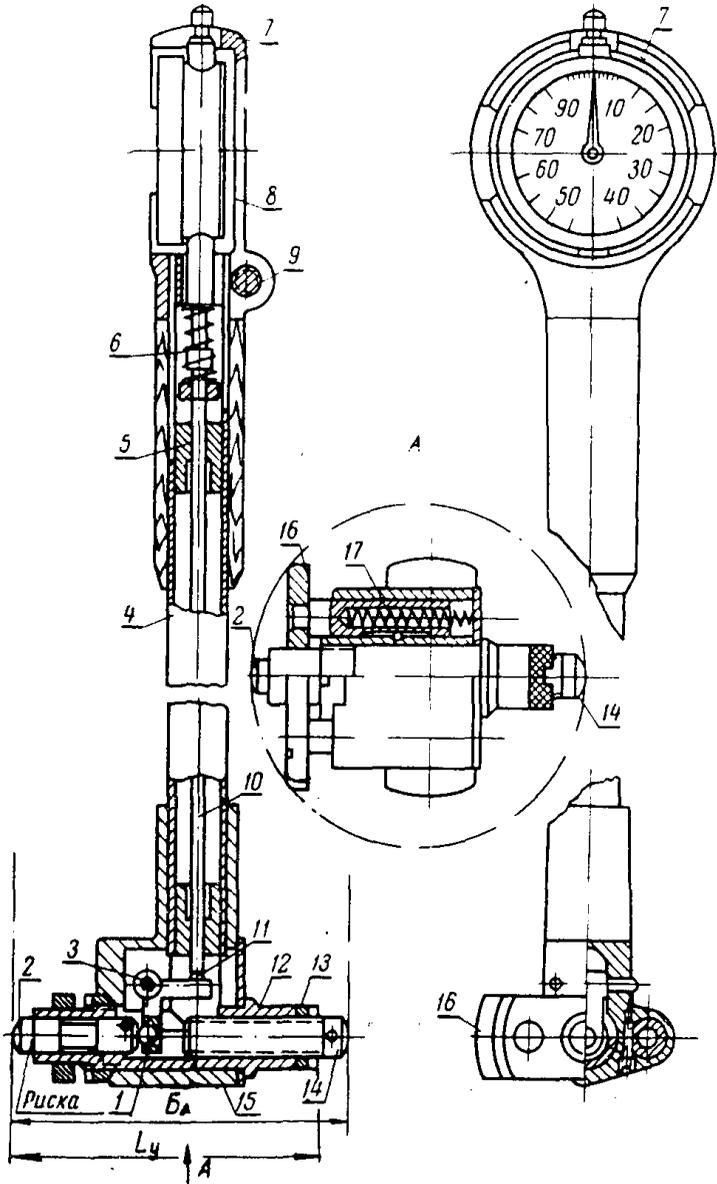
Индикаторный нутромер с рычажной передачей
